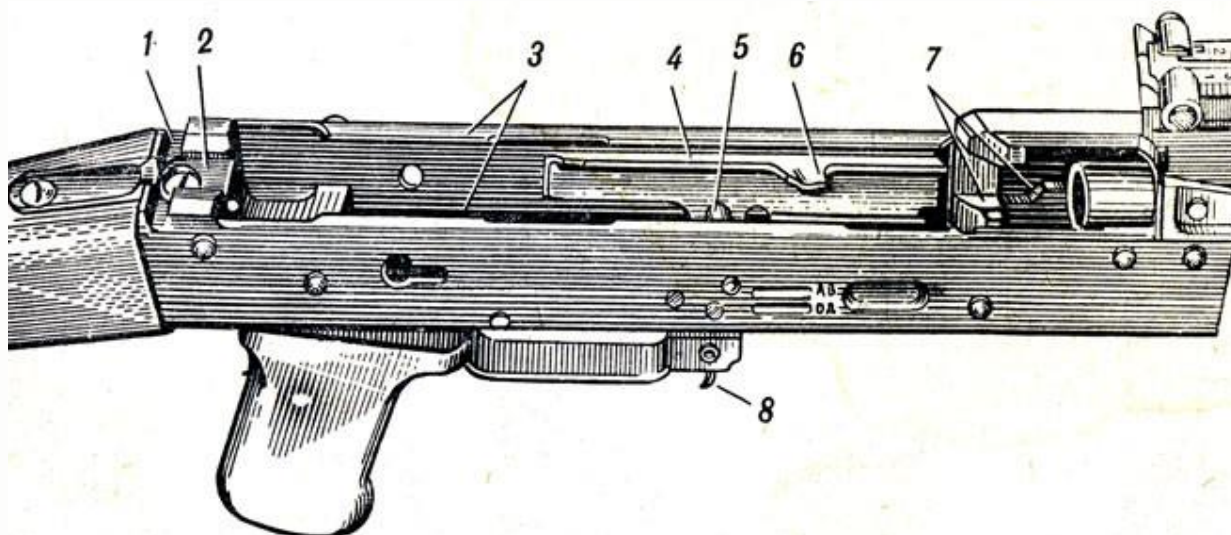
Ствольная коробка: 1 — поперечный паз; 2 — продольный паз; 3 — отгибы; 4 — направляющий выступ; 5 — перемычка, 6 — отражательный выступ; 7 — вырезы; 8 — защелка магазина
